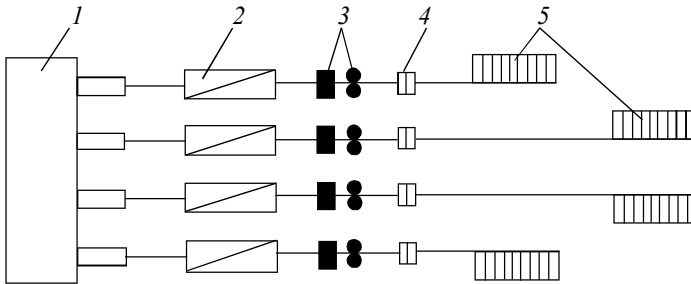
Схема расположения оборудования заготовочного литейно-прокатного агрегата:
